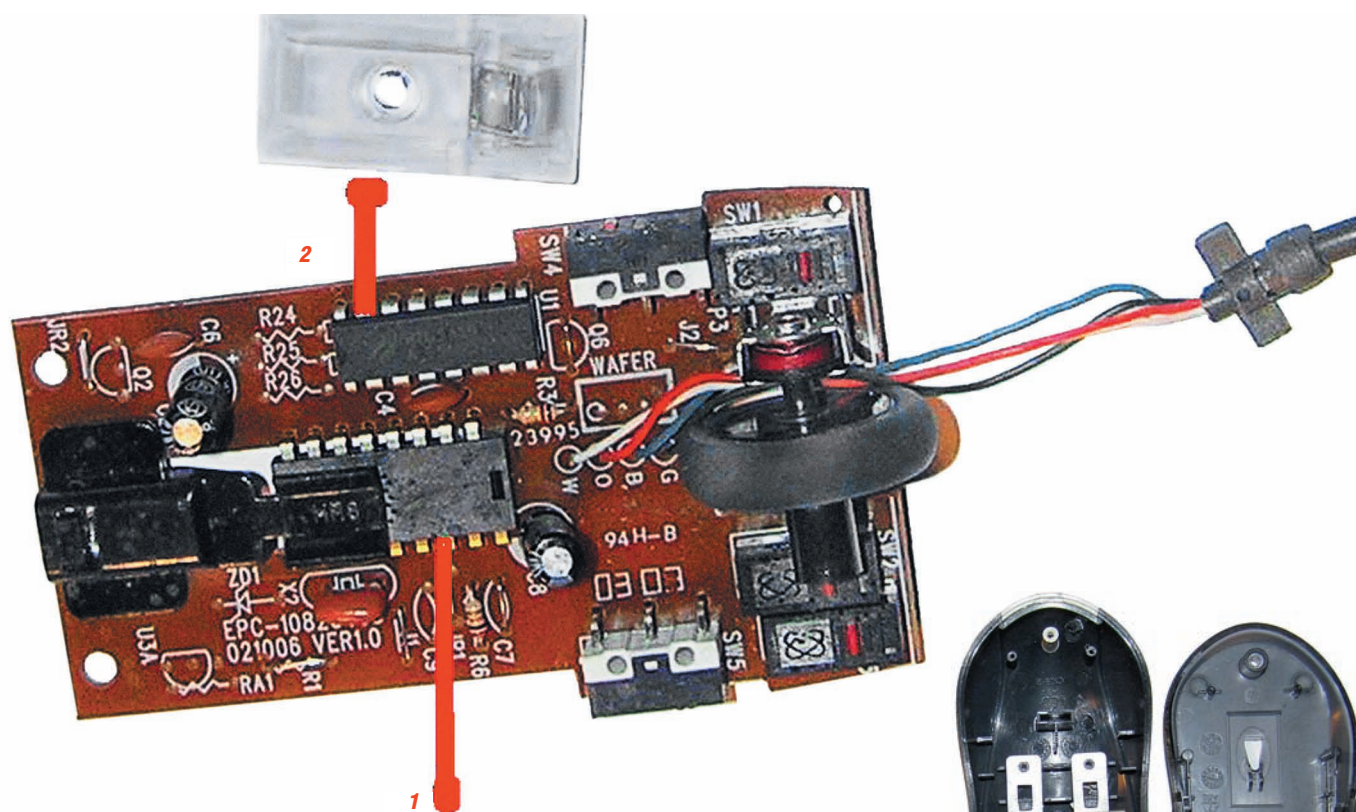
Вид печатной платы оптической мыши Defender Optical 1330 со снятой крышкой корпуса
